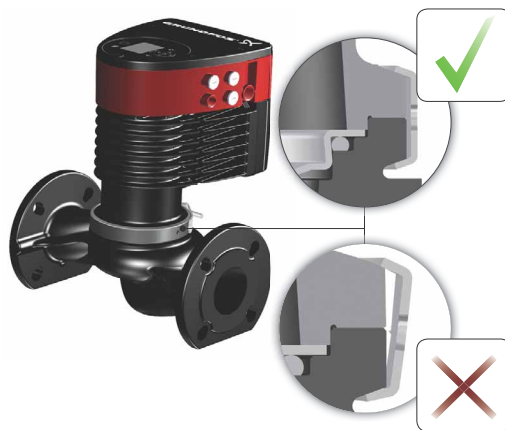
Instalación del cabezal de la bomba en la carcasa de la bomba
